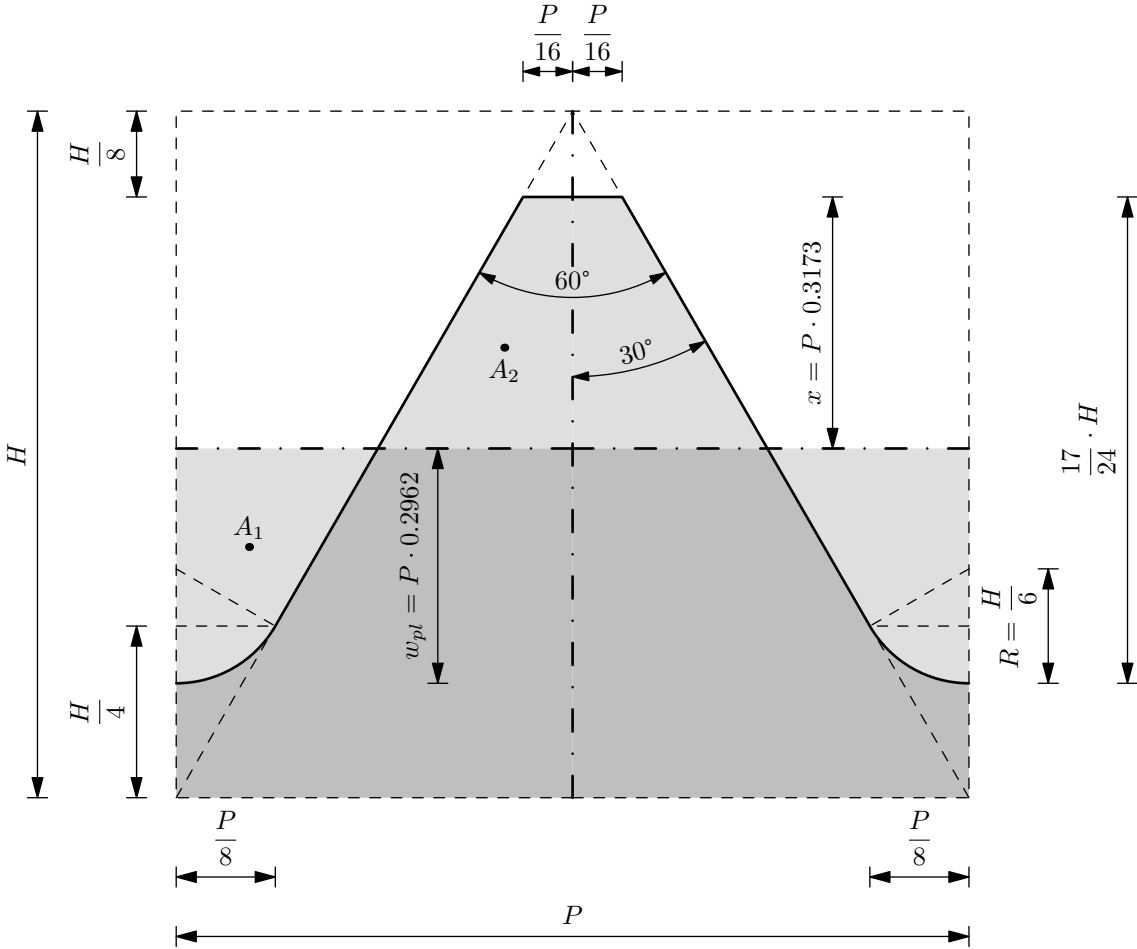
Gewindeform senkrecht zur Gewindeachse
